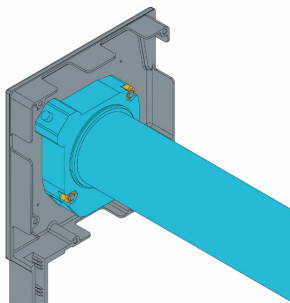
Внутривальный привод в сборе с крышкой боковой роллетной
